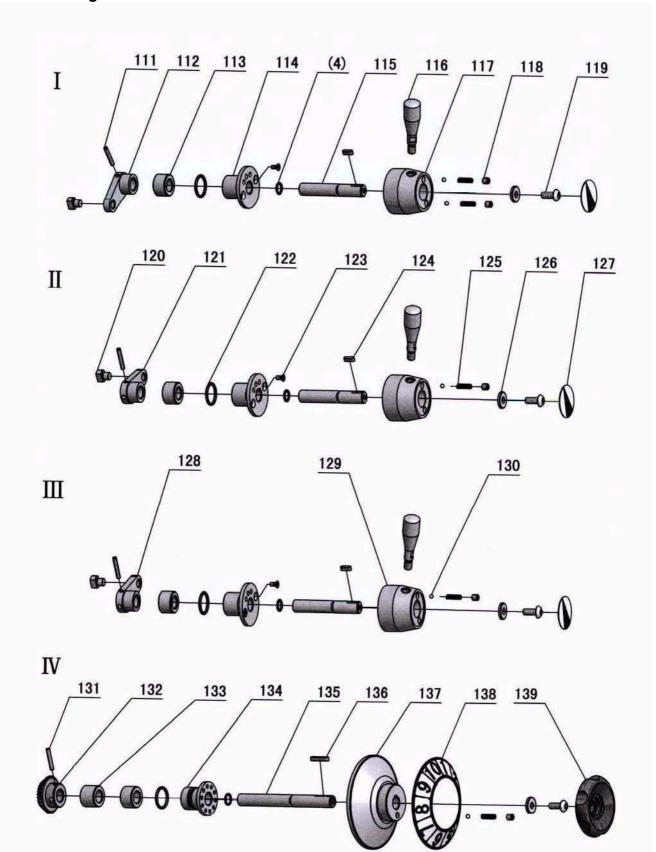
Vorschubgetriebe 4 von 4 - Headstock feed gear 4 of 4
